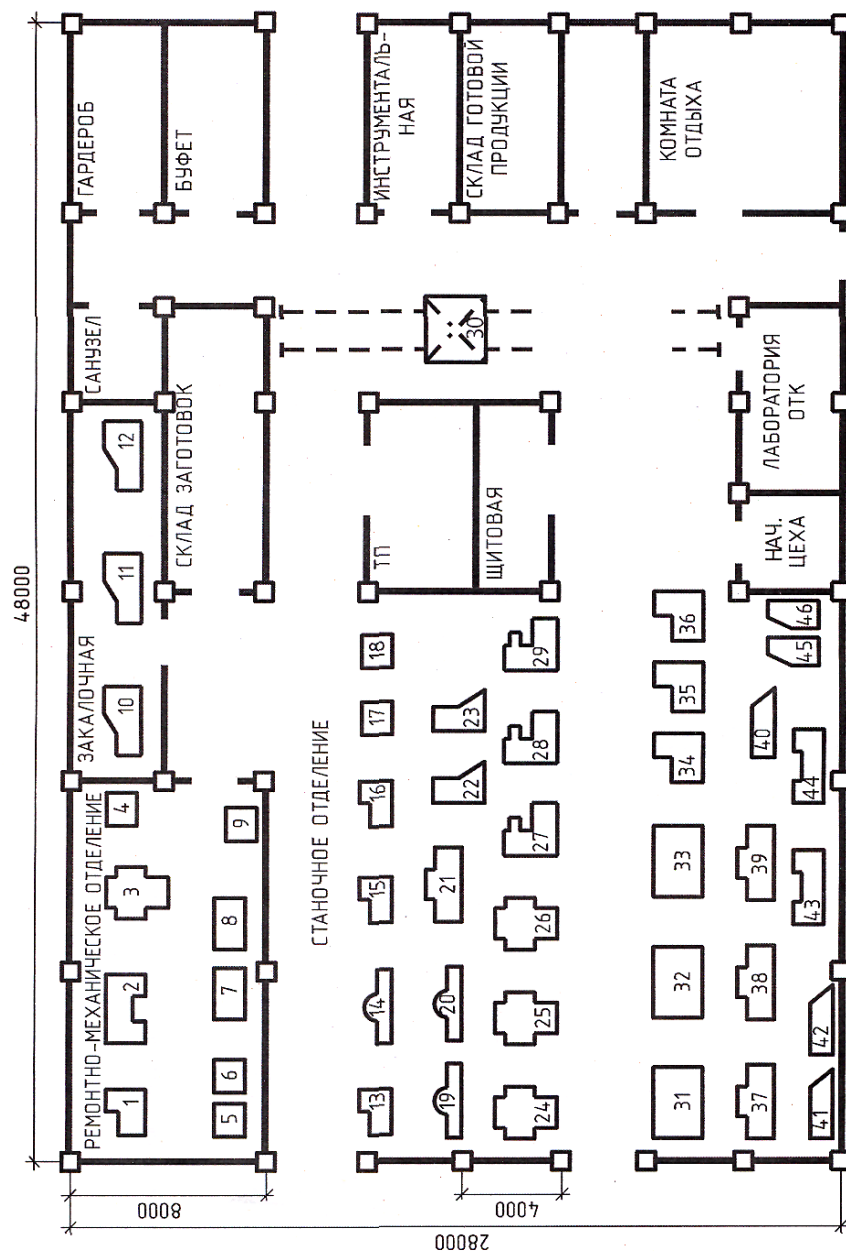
План расположения ЭО цеха механической обработки деталей
